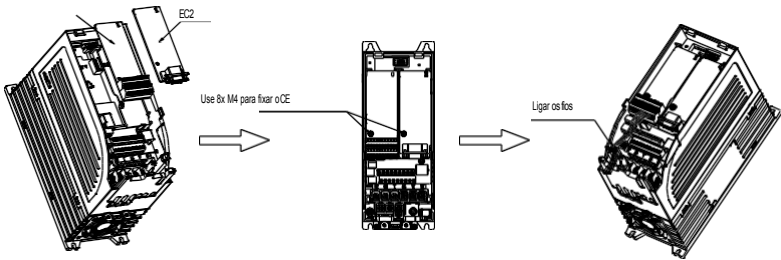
VFDs de 1,5 a 7,5 kW com placas de expansão instaladas
